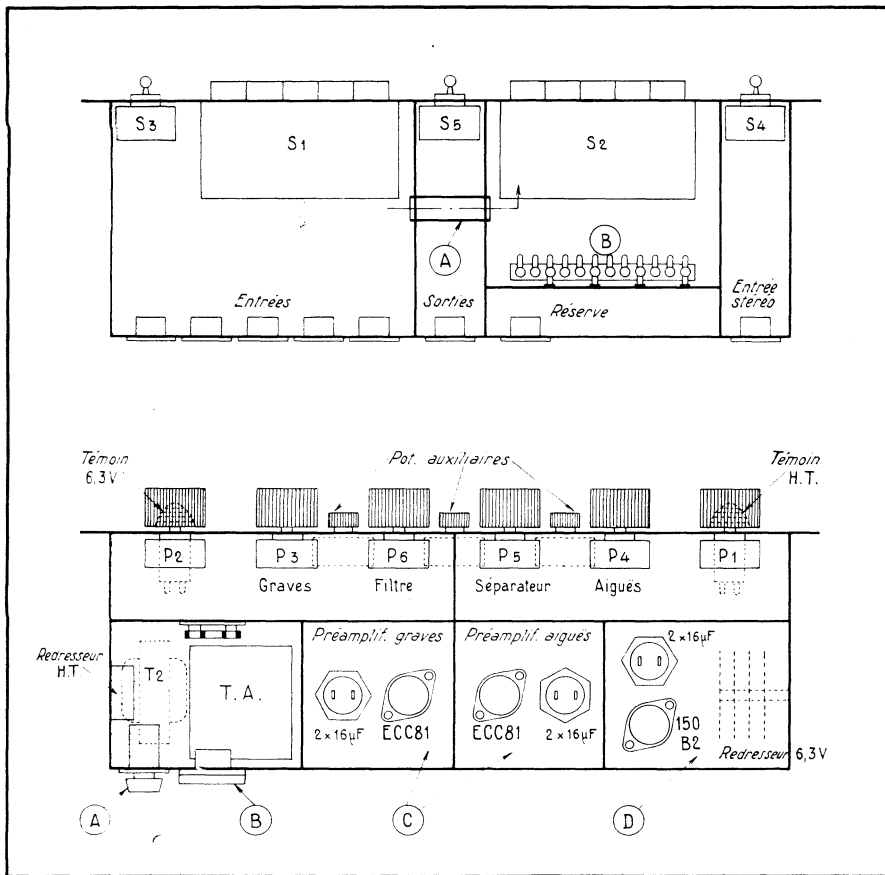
Disposition des pièces sur le châssis inférieur (en haut) et le châssis supérieur (en bas).
